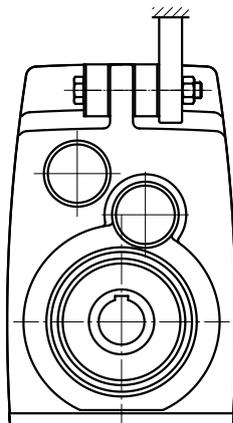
Redutor fixo com elemento de fixação sobre eixo sem face de encosto
